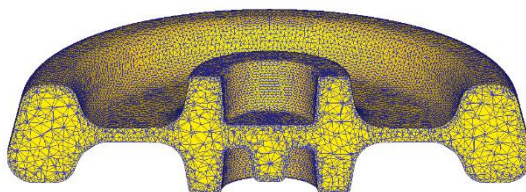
Конечно-элементная модель заготовки железнодорожного колеса (заготовка после формовочного пресса силой 100 МН).
